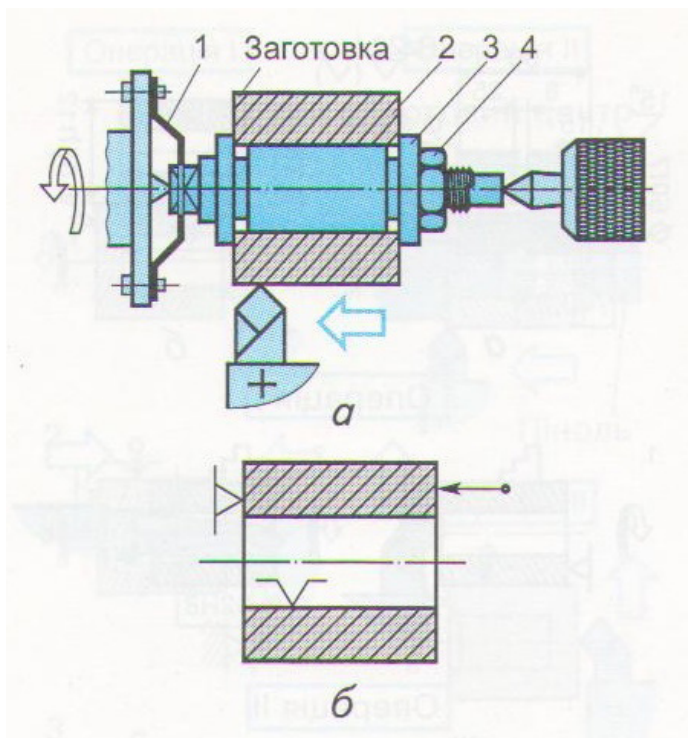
Закріплення заготовки втулки на циліндричній оправці (а) та умовне позначення (б):
